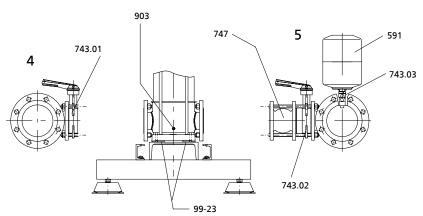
Gesamtzeichnung Hyamat SVP Eco mit Movitec 25, 40, 60, 90
